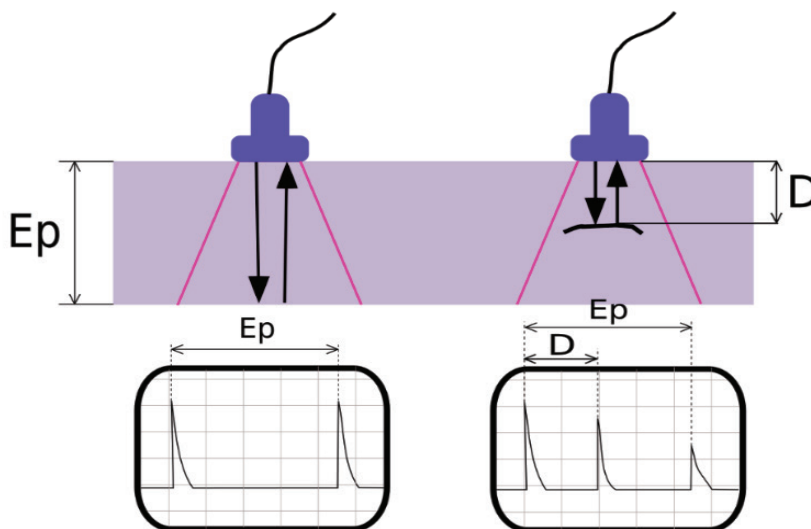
Принцип ультразвукового контроля: E_p — толщина заготовки, D — расстояние до дефекта
